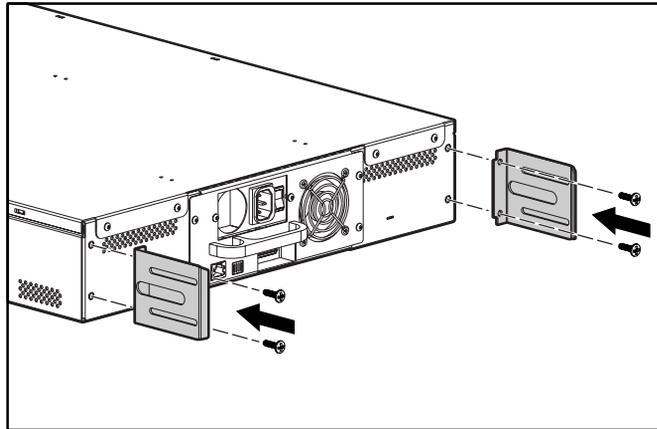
Montaggio delle staffe di supporto di SuperLoader
